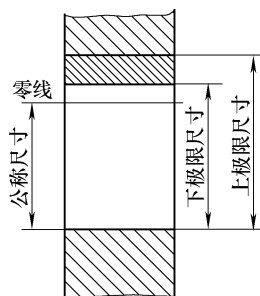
公称尺寸、上极限尺寸和下极限尺寸
